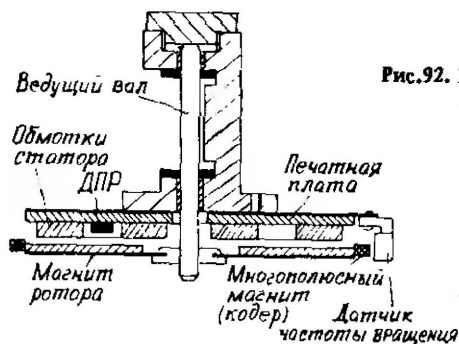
Конструкция ведущего вала R-DAT-магнитофона
